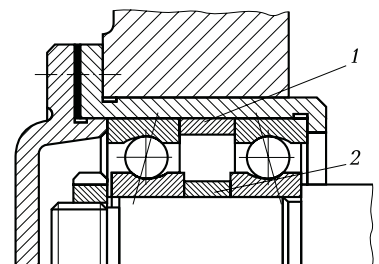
Схема подшипниковой сборочной единицы, позволяющей регулировать радиальные зазоры в опорах:
